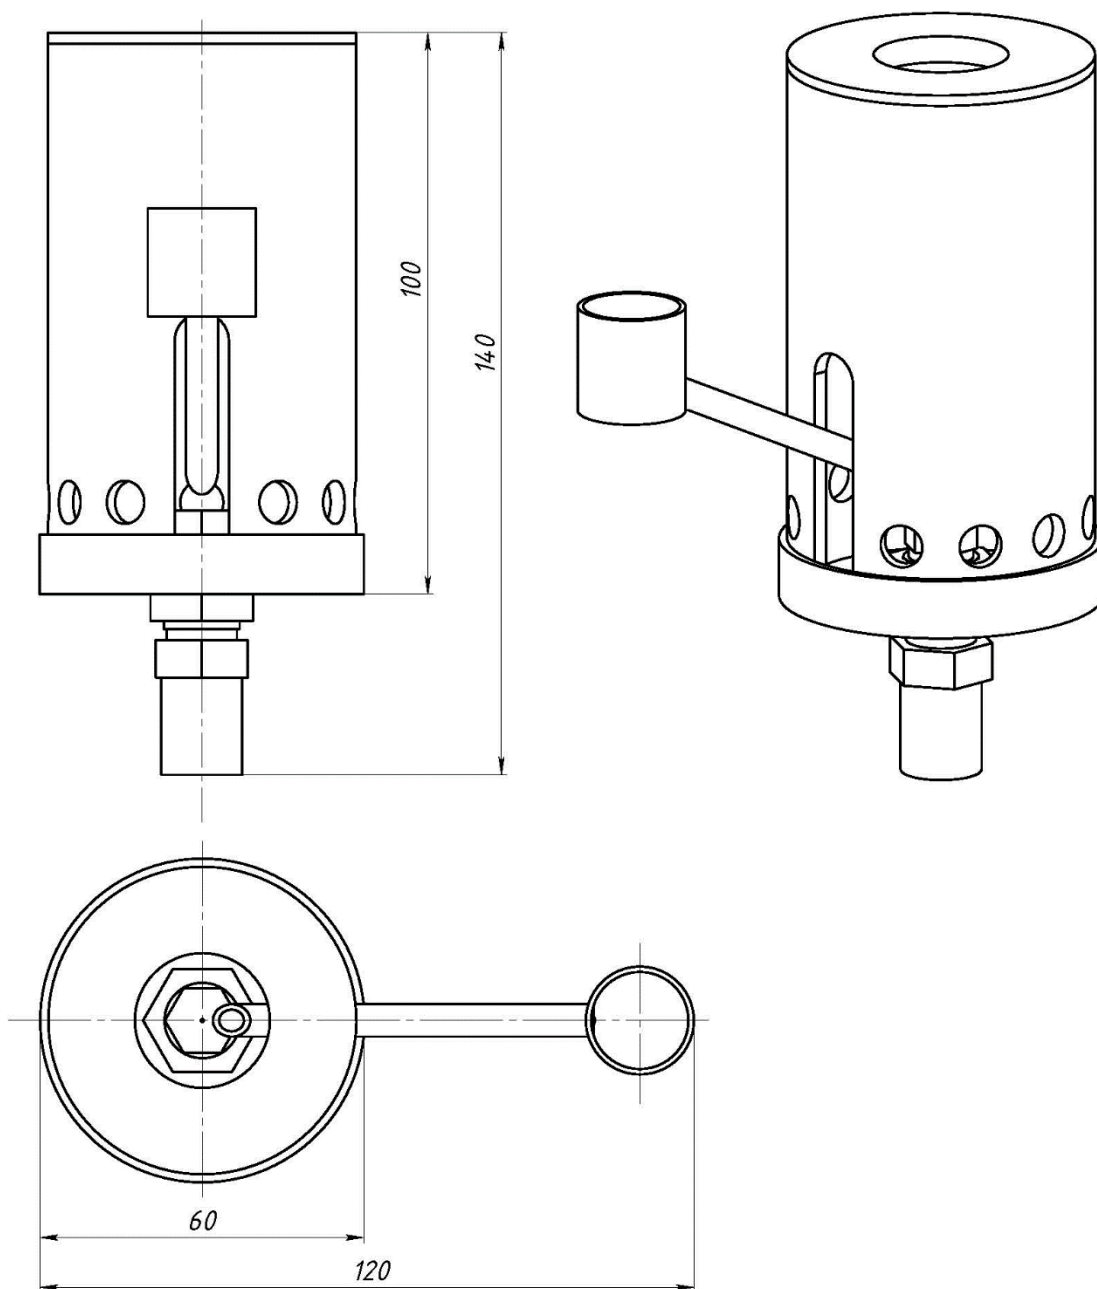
Чертеж общего вида на горелочное устройство
